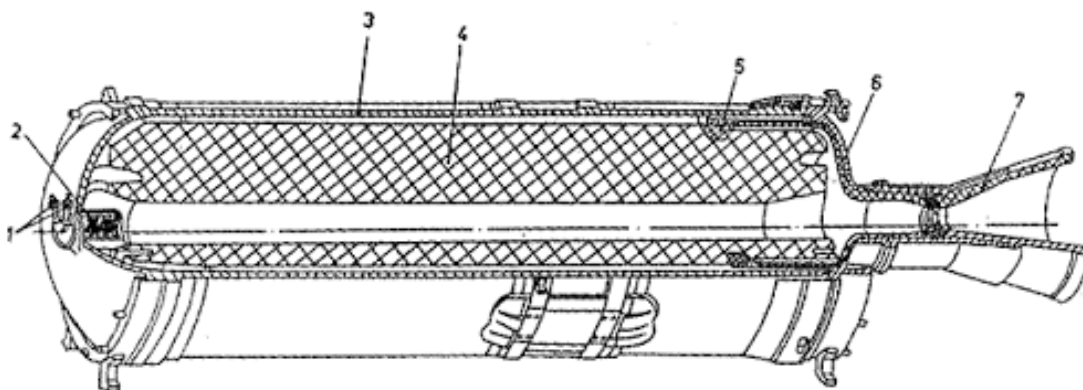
Конструкція РДТП: 1-піропатрони; 2-підпалювач; 3-корпус; 4-паливний заряд; 5-вузол кріплення ПЗ; 6-дно; 7-сопловий блок.
